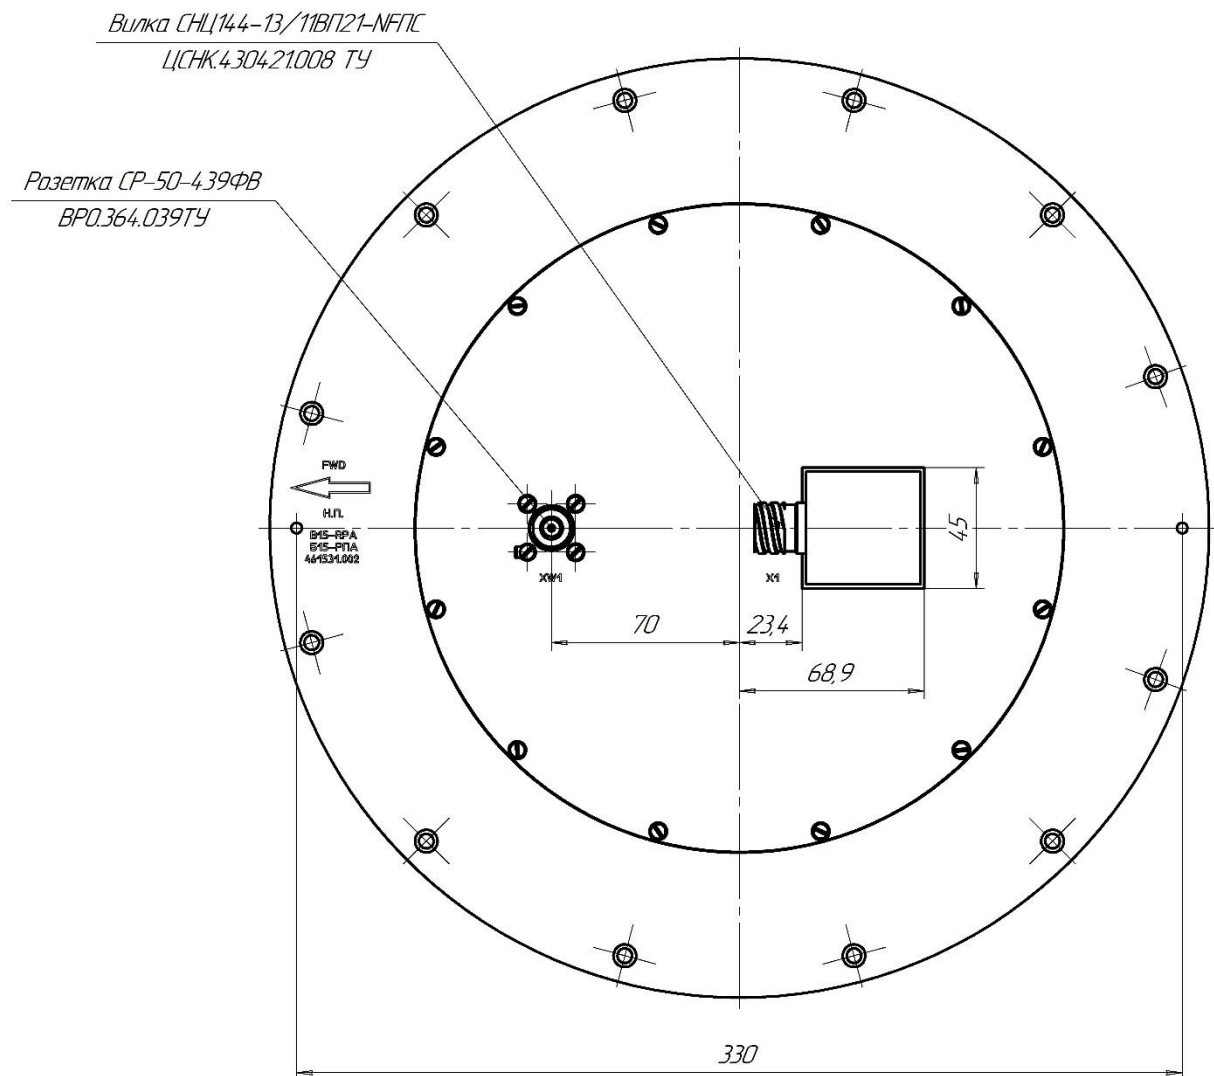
Габаритный чертеж блока Б15-РПА
